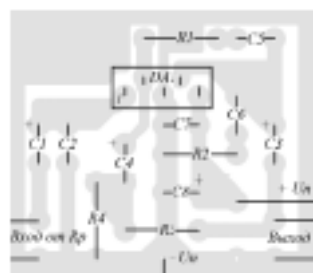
Эскиз монтажной платы монофонического УЗЧ. Вид со стороны установки деталей
